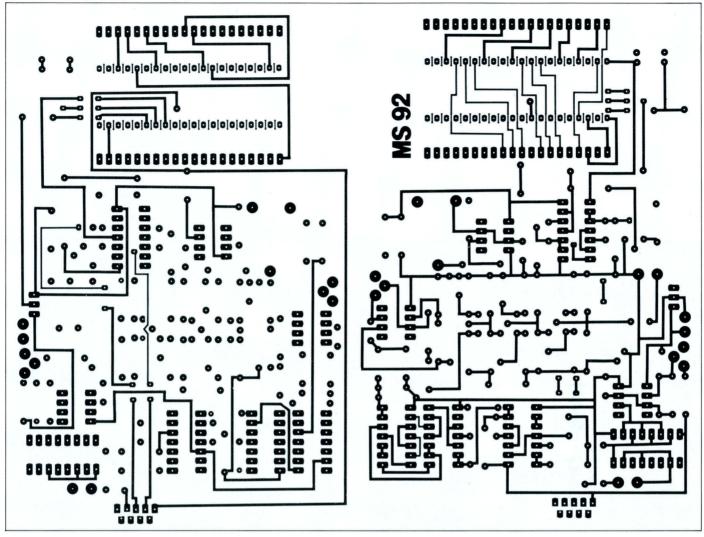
a) Circuit imprimé vu côté soudures. – b) Vu côté composants.
